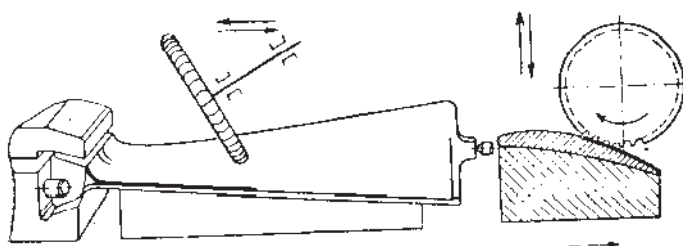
Схема роздільного фрезерування корита і спинки пера лопатки подовжніми строчками
